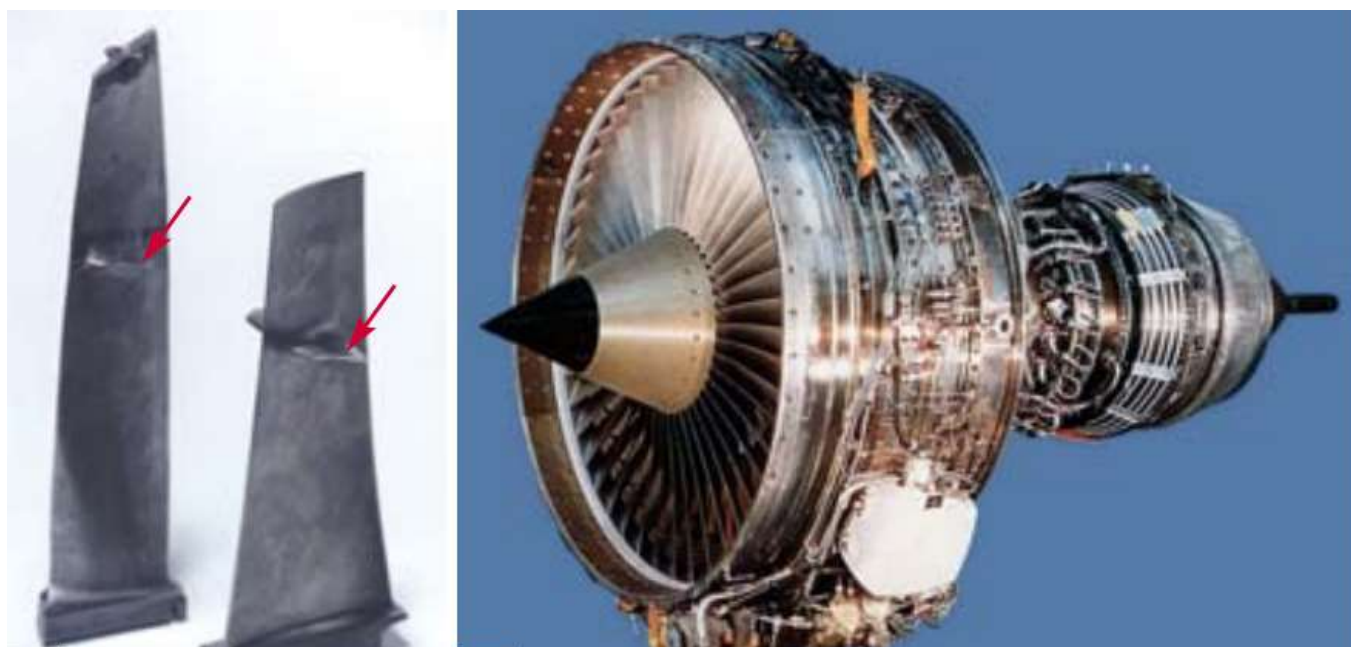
Лопатки (а) компресора авіаційного двигуна (б), зміцнені металокерамікою WC+Co (місця з покриттями вказано стрілками) [10]
